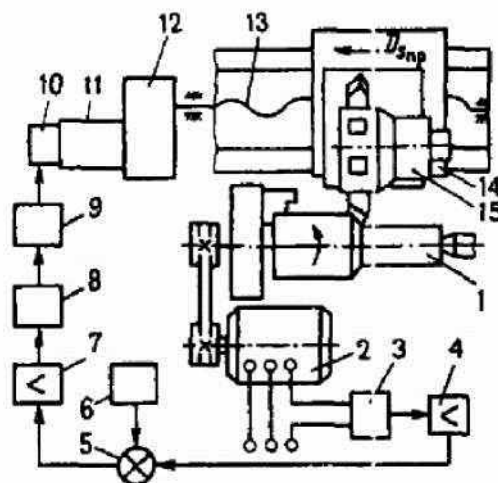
Схема обробки заготовки на токарному верстаті з адаптивною системою ЧПК
